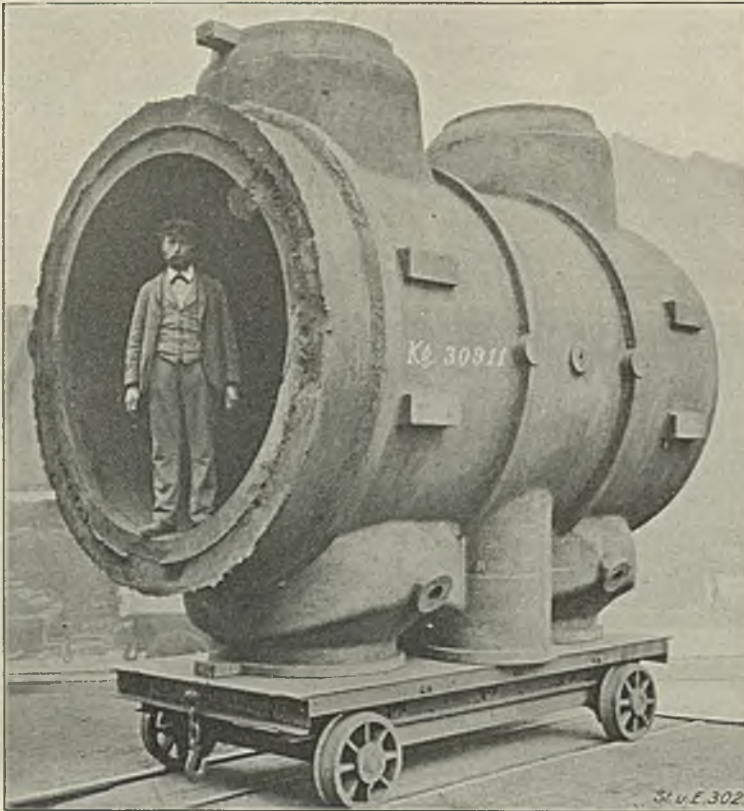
Niederdruckzylinder einer 6000pferdigen Ventilmaschine.
